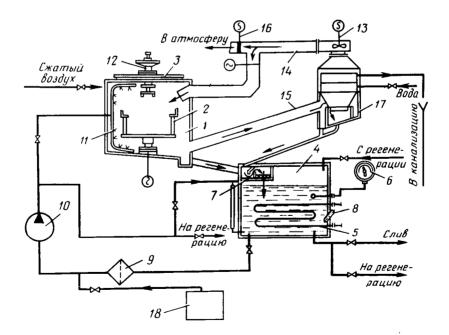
Установка мойки деталей и компрессора в сборе в органическом растворителе:
